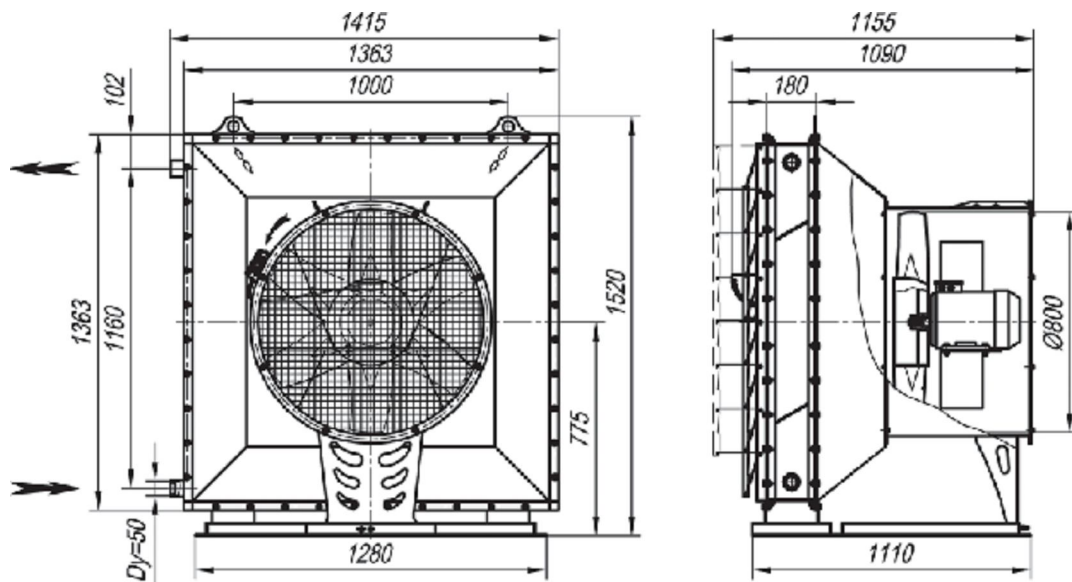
Габаритные и присоединительные размеры агрегата воздушно-отопительного СТД-300 на базе водяного калорифера типа КСК.
